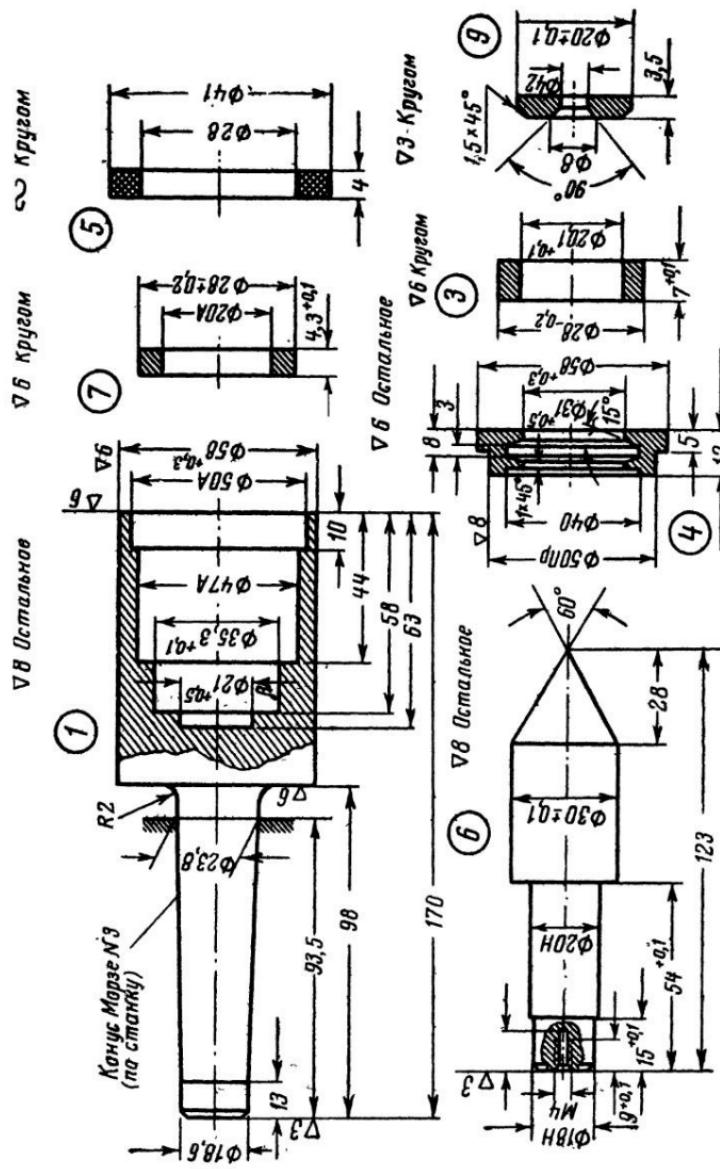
Детали вращающегося заднего центра: 1 — корпус; 3 — кольцо; 4 — крышка; 5 — сальник; 6 — центр; 7 — колыто; 9 — шайба.
